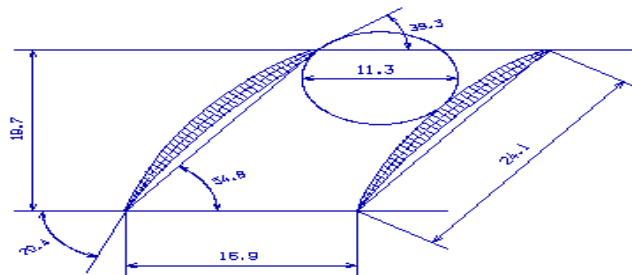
Решетки профилей рабочего колеса компрессора
